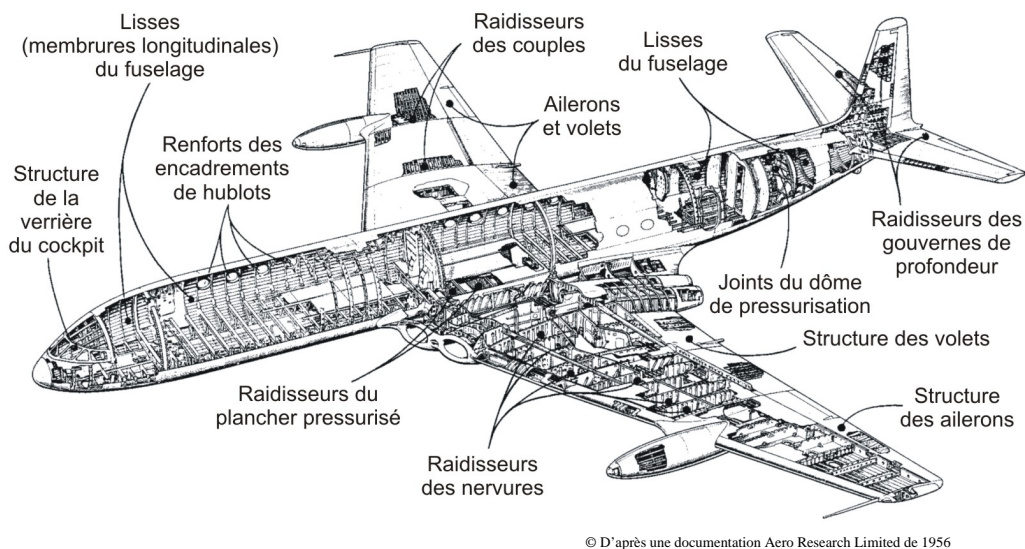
Exemples de pièces assemblées par collage avec l'adhésif Redux® sur le quadrimoteur De Havilland Comet.
